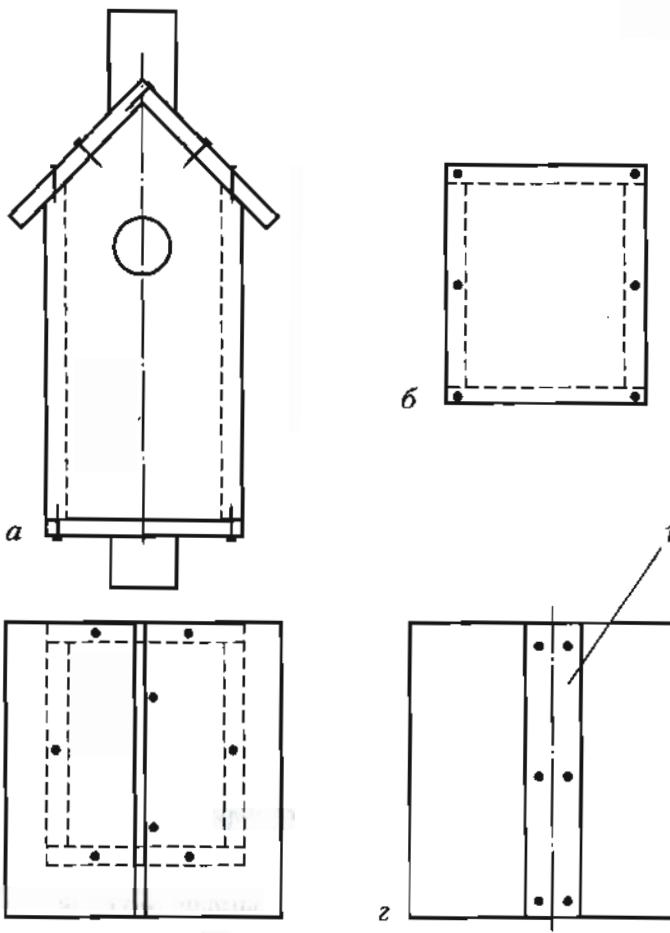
Схема сборки домика для птиц: а – главный вид, б – вид снизу, в – вид сверху (крепление крыши), г – вид сверху (1 – конёк)
